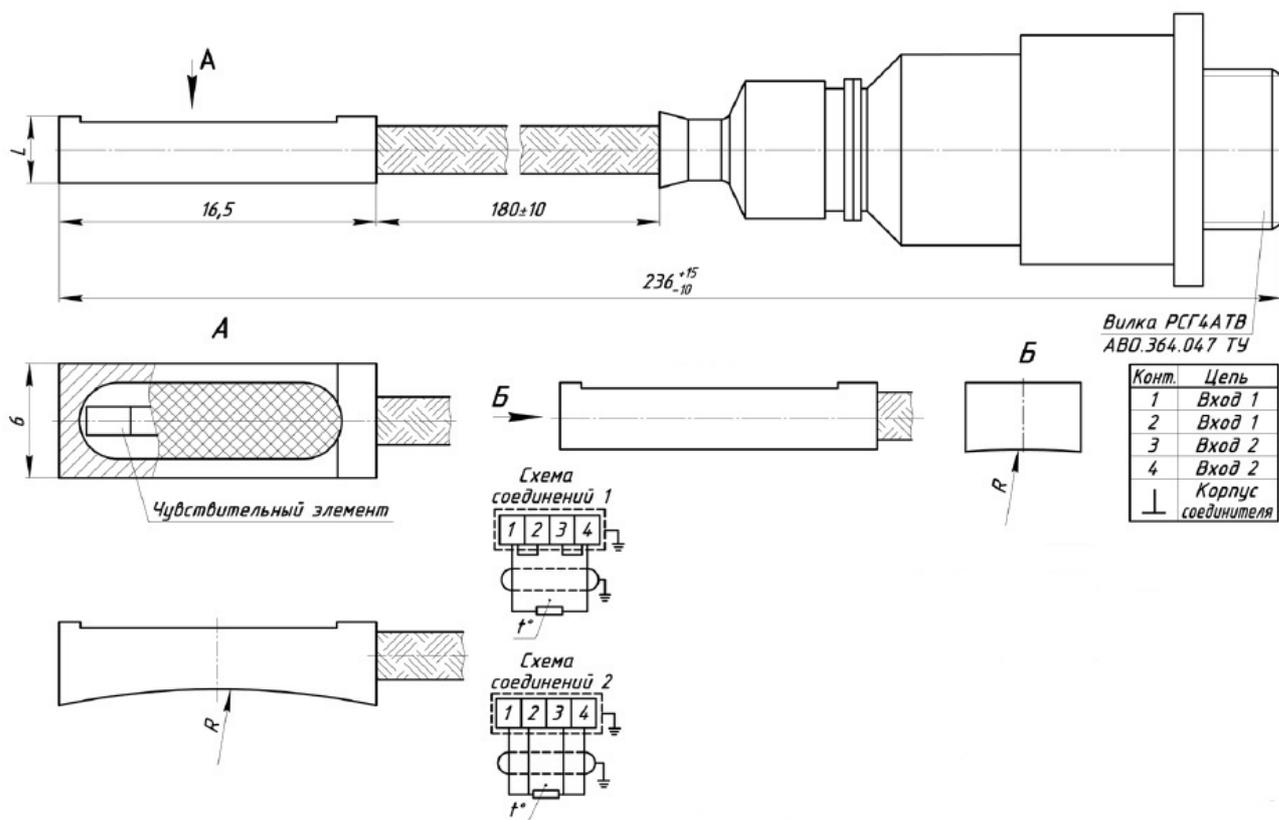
Габаритно-установочные размеры термопреобразователя
